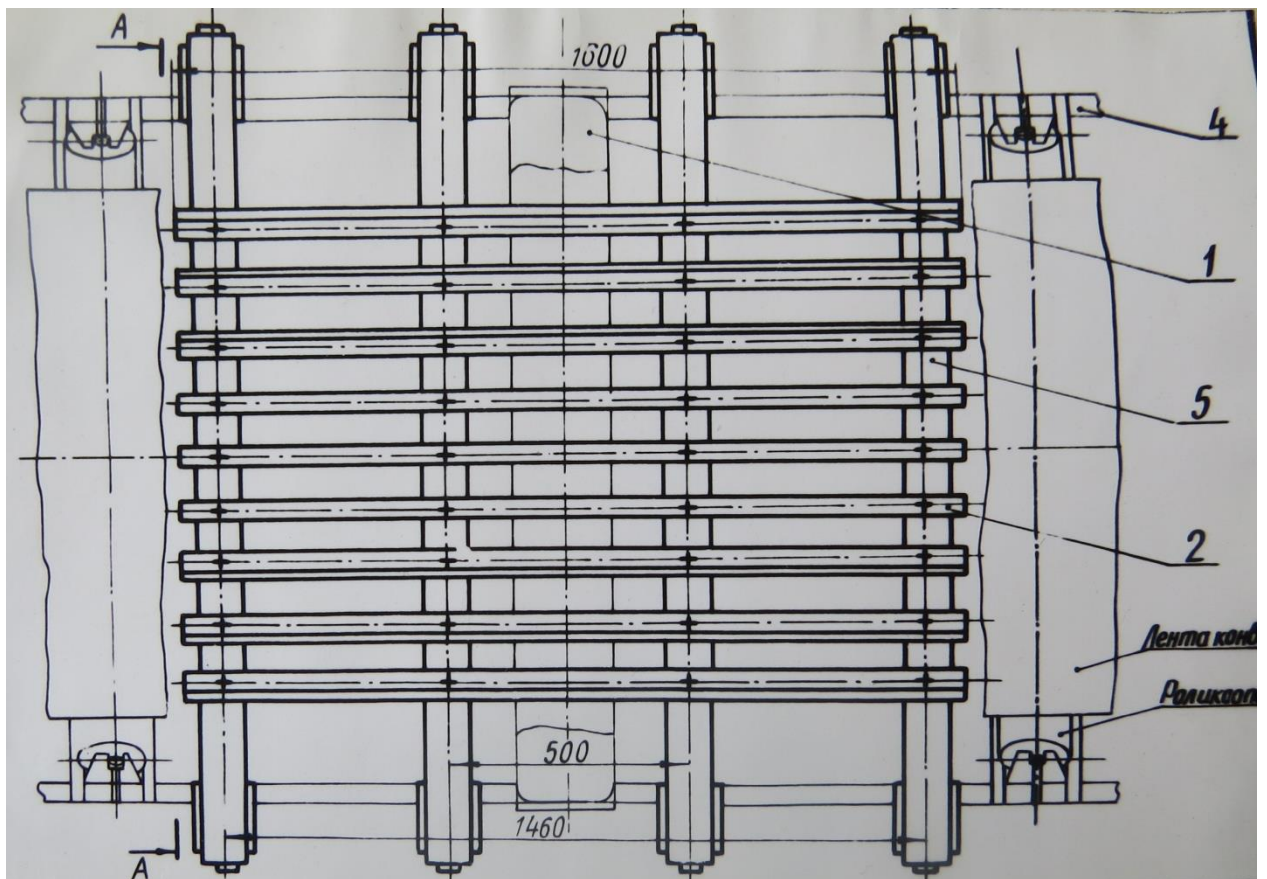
Схема установки опор ковзання металошукача:
